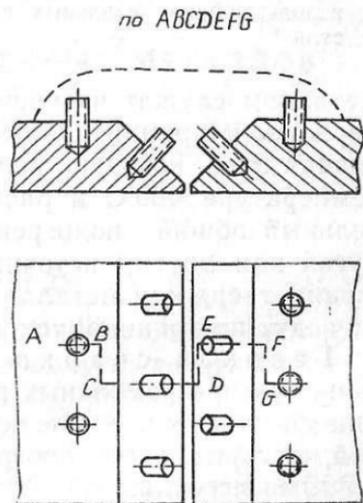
Схема сварки чугуна стальным электродом с применением шпилек
